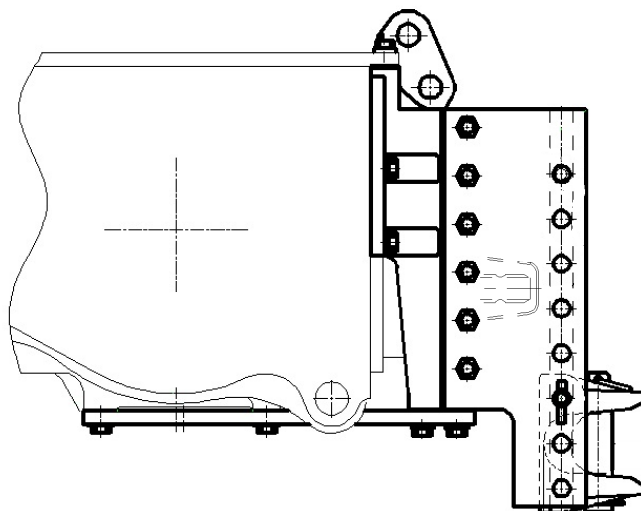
Схема установки вилки не вращающейся
